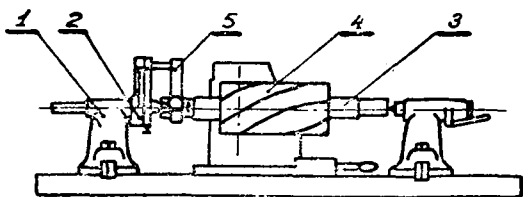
Установка приспособления для заточки фрезы по заднему углу
